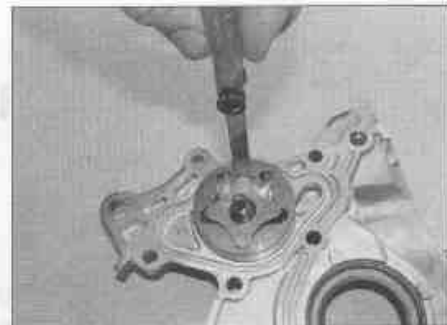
,б. ...и зазора по головкам зубьев роторов
